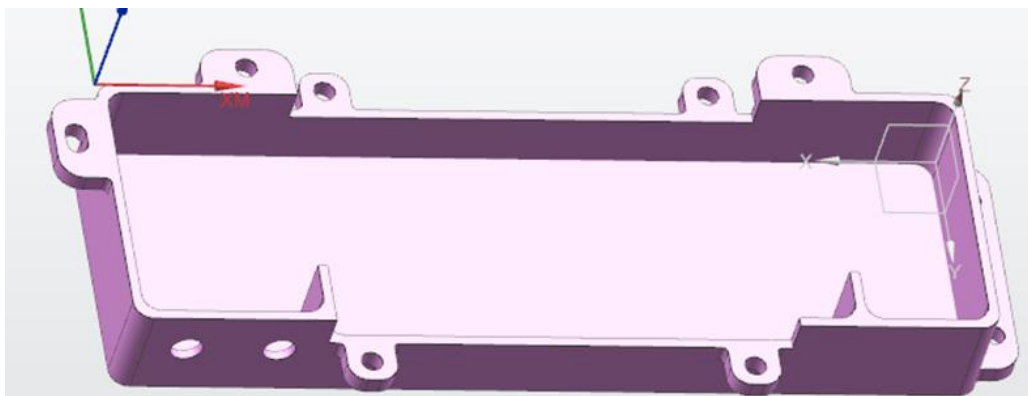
Трехмерная твердотельная модель корпусной детали из капролона
